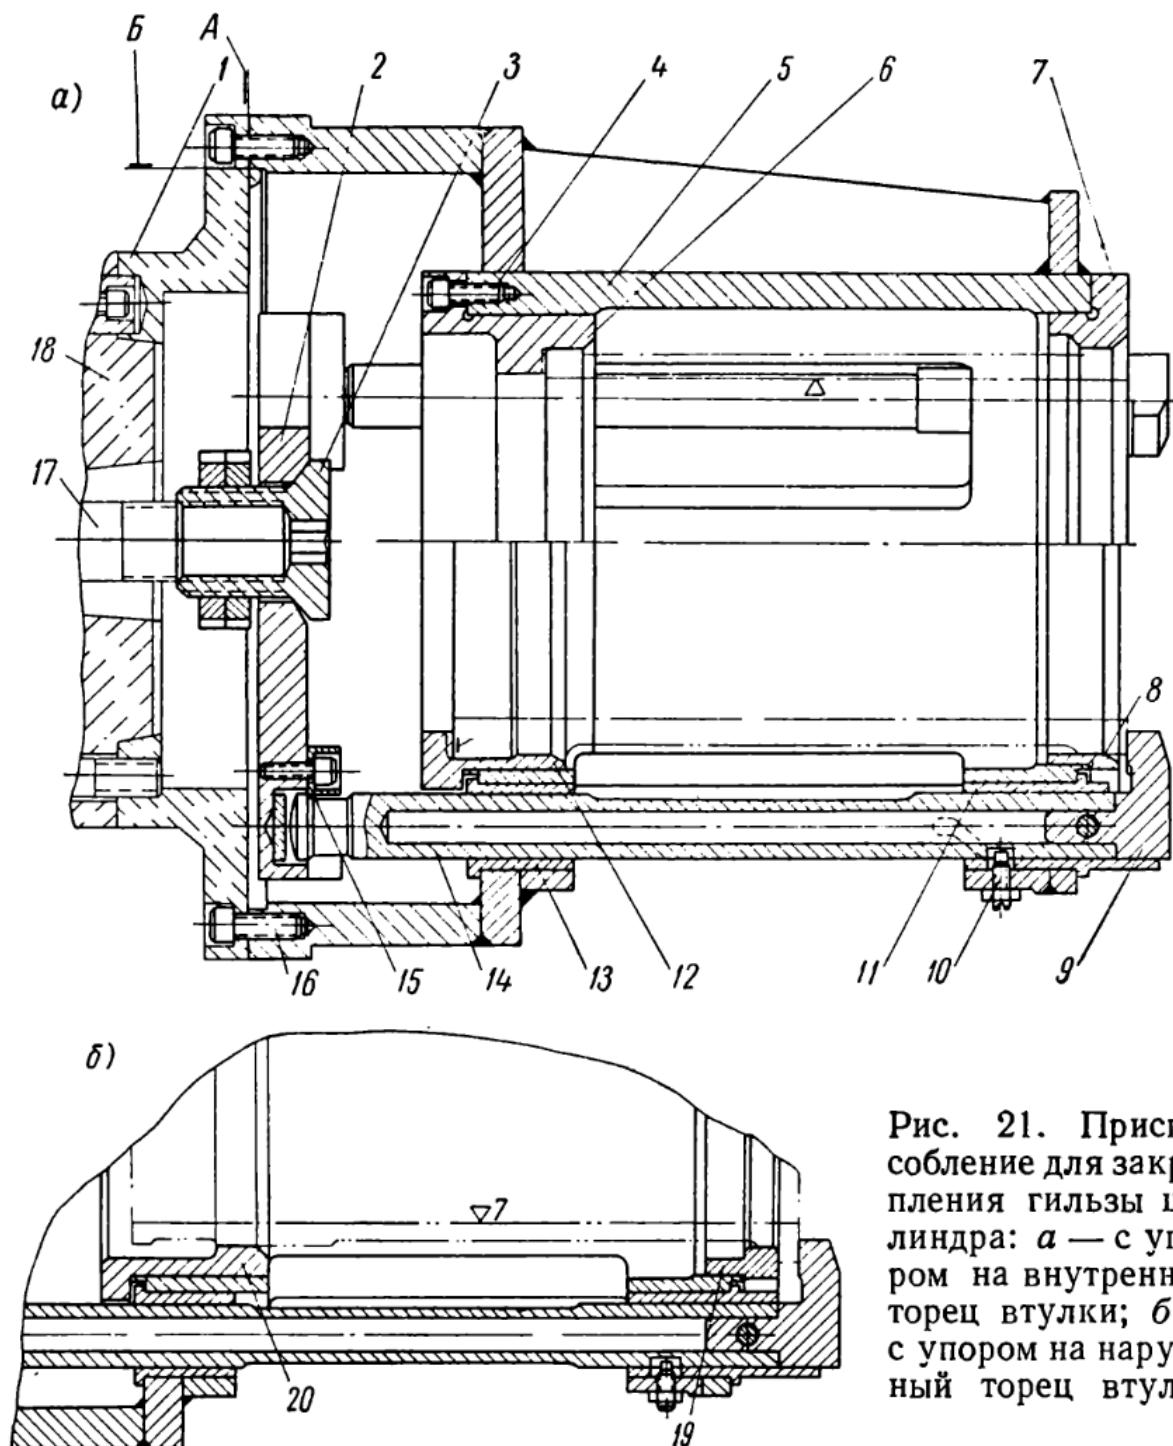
Приспособление для закрепления гильзы цилиндра: а — с упором на внутренний торец втулки; б — с упором на наружный торец втулки
